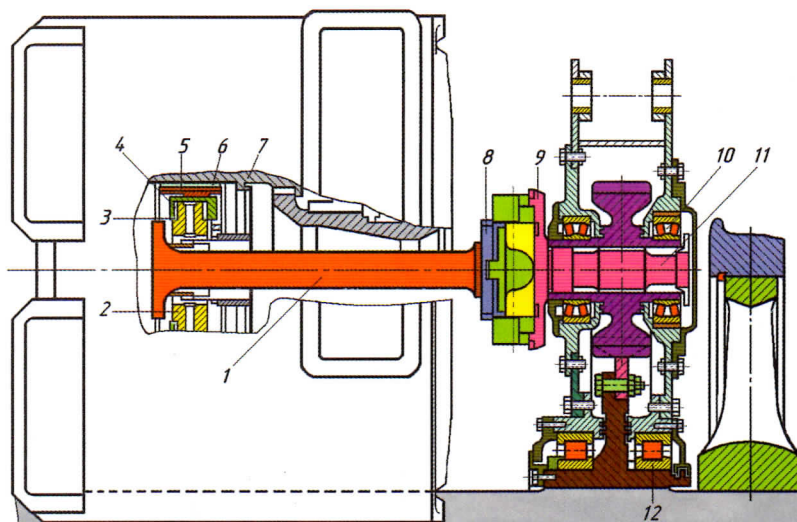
Редуктор и карданный привод II класса электровоза ЧС4:
